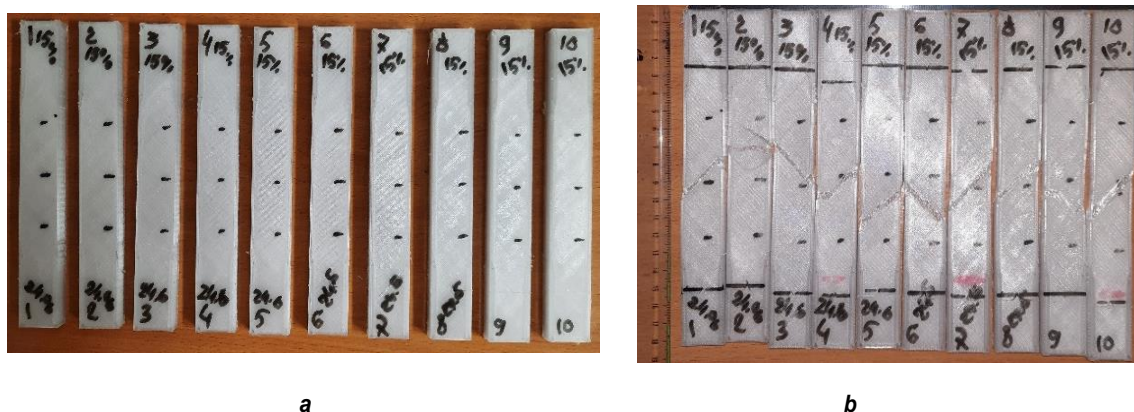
Образцы для испытаний на растяжение: а – образцы до испытаний; б – образцы после испытаний
